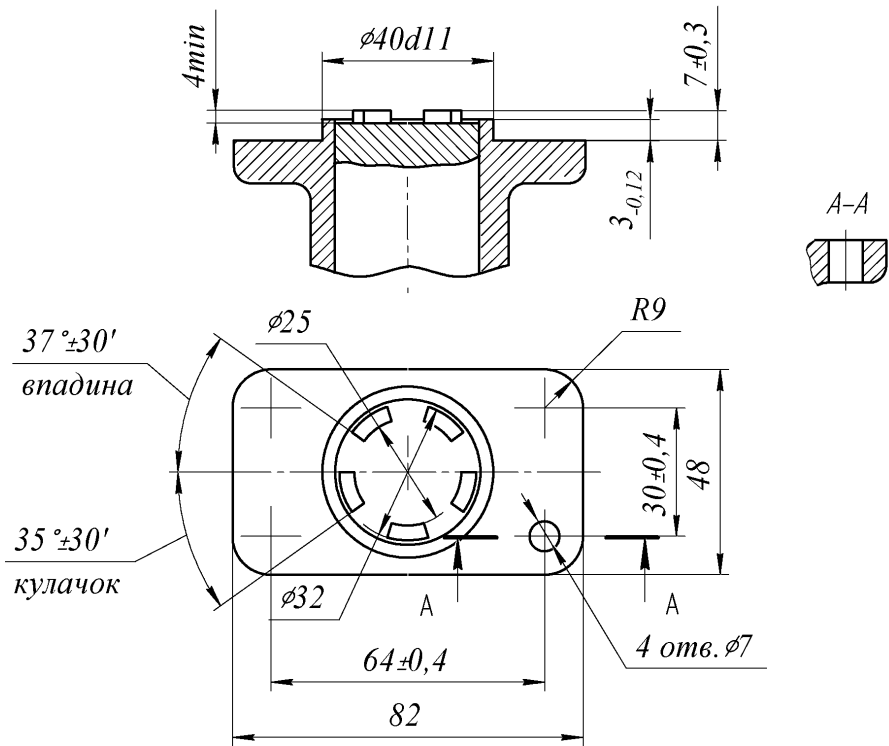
Ответное присоединение трубопроводной арматуры типа МК
